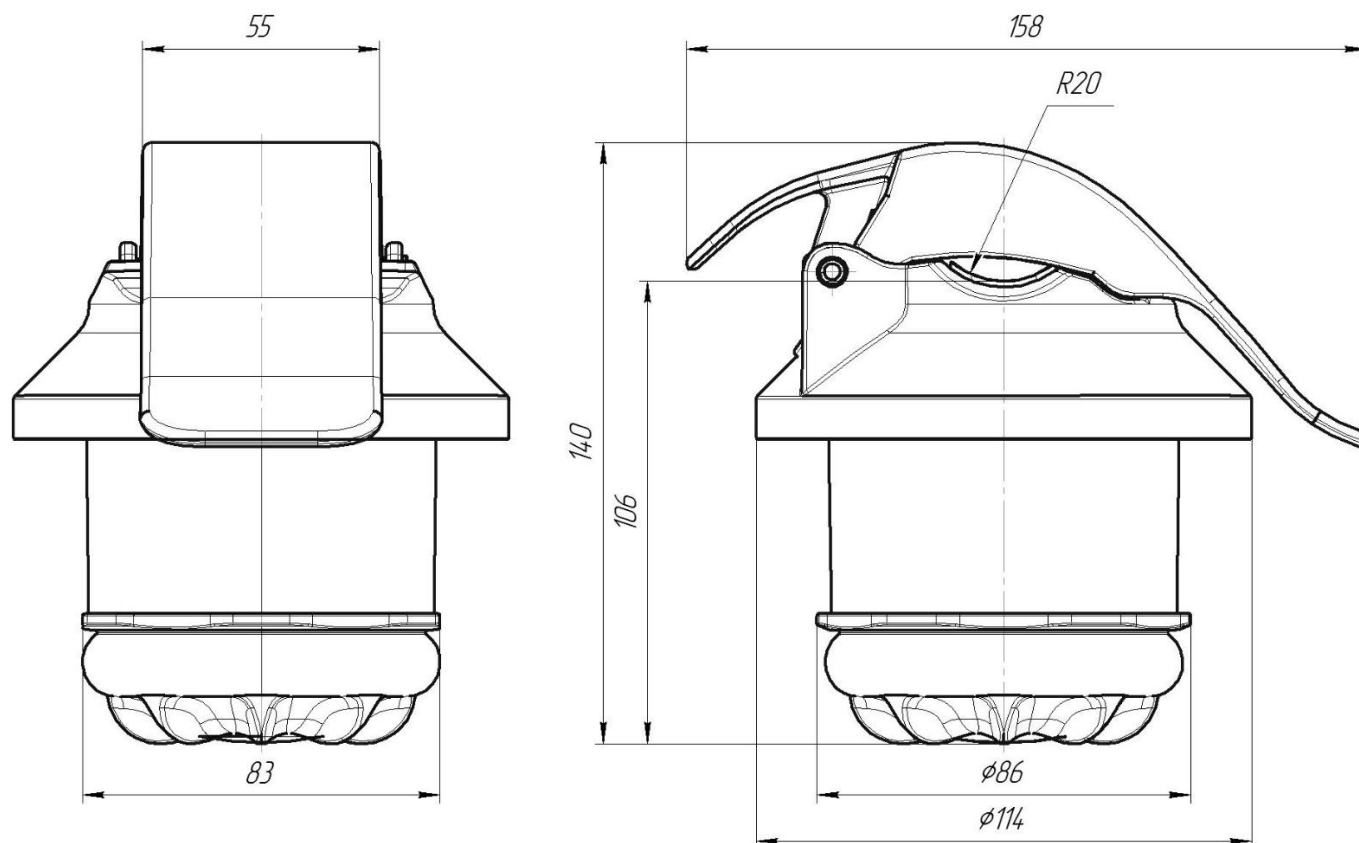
Габаритные размеры индикатора ИКЗ-В3хЛ
